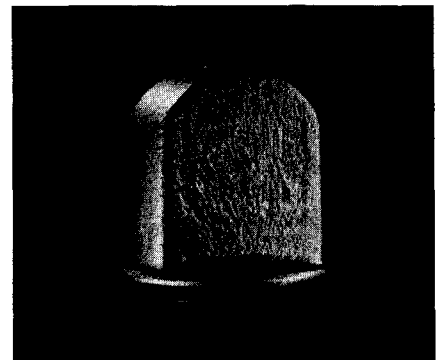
Zylinderboden aus St 37 (1,45 kg). Das Blatt ist mit geringem Konus geschmiedet. Flanschseitig wird ein kreisrunder Sitz mit dem Innen-Ø des Zylinderrohres als Zentrierung für das automatische Verschweißen beider Teile eingeschmiedet und anschließend kalt kalibriert.
